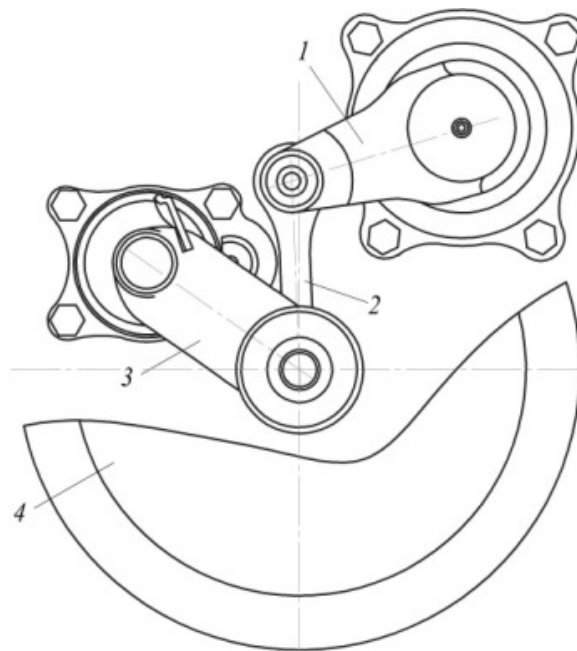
Кинематика узла подвески ходовой части танка Т-72:
